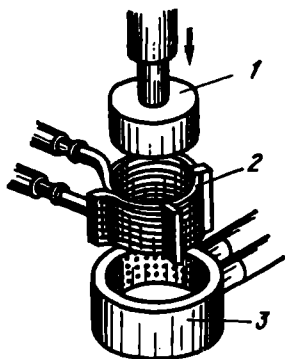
Поверхностная закалка с нагревом токами высокой частоты:
